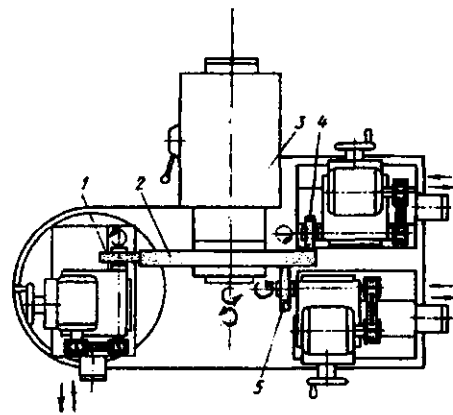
Установка для предварительной правки шлифовальных кругов перед балансировкой
